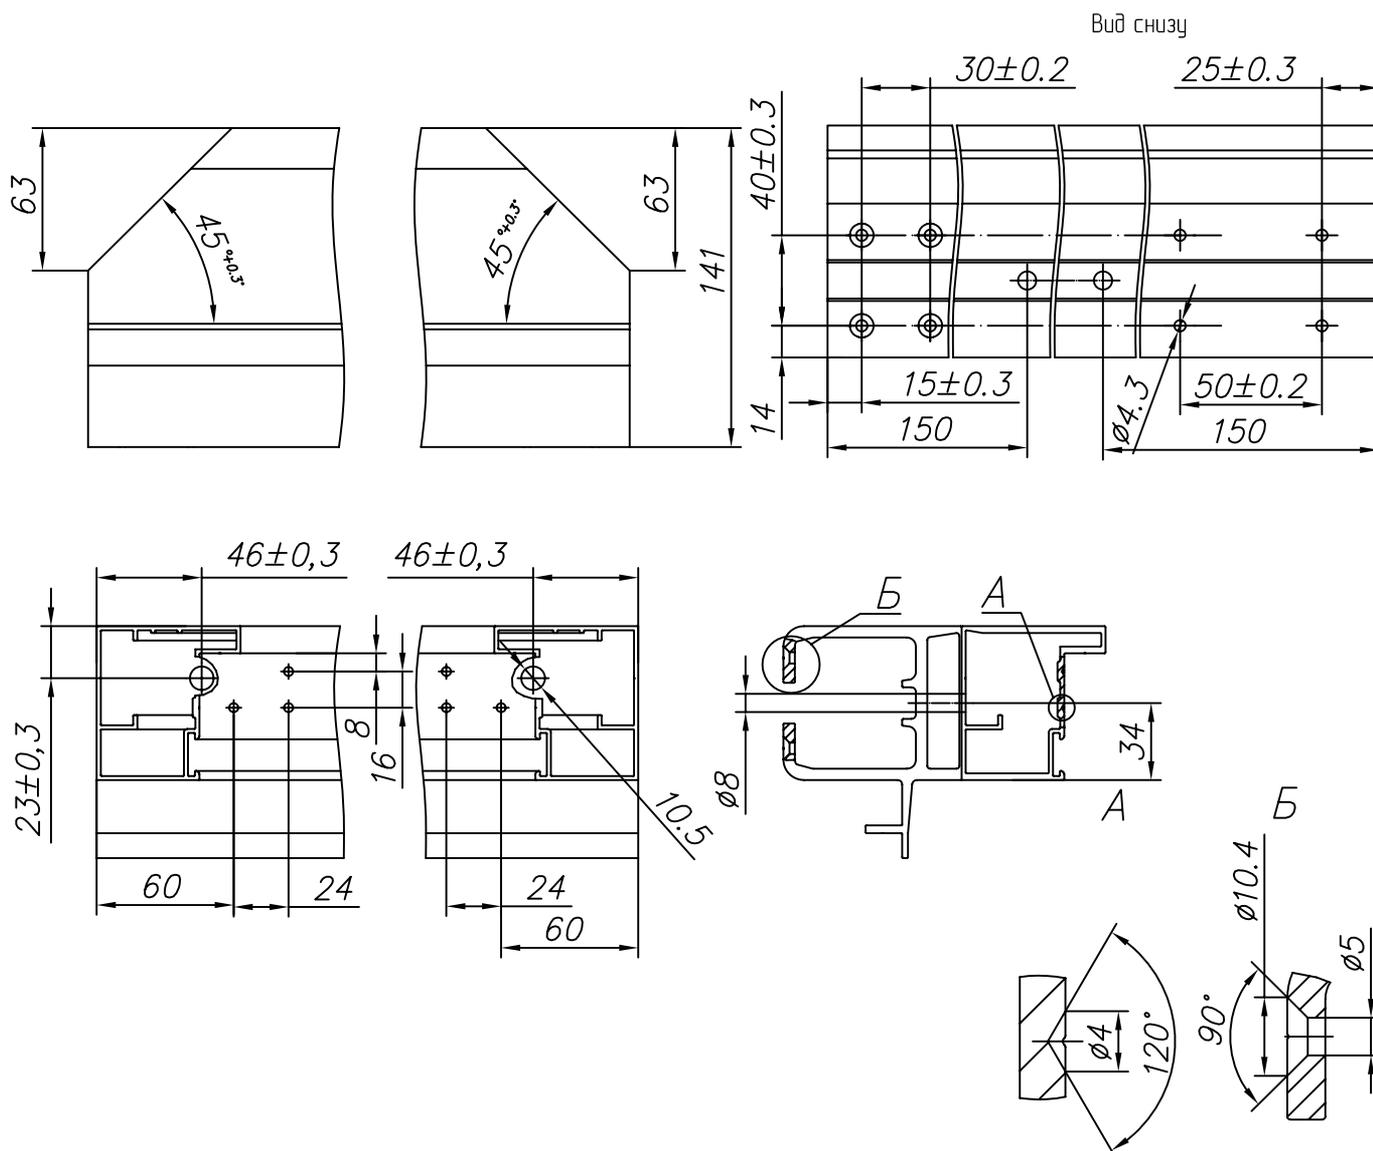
Изготовление шины для пассивной(опорной) створки (открытие влево)
